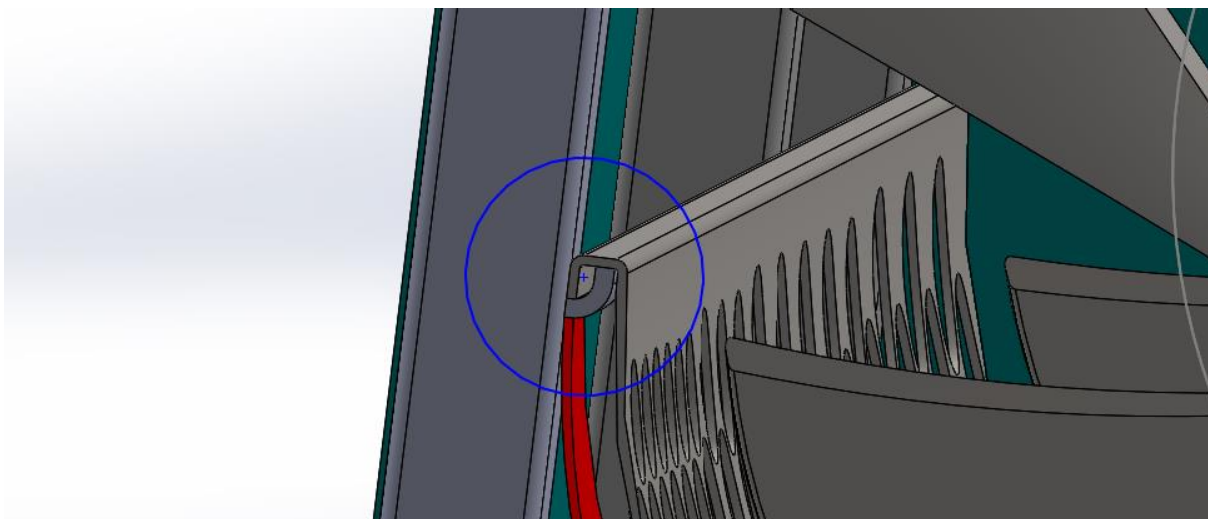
Detail vyspárování prostoru kolem podávacího šneku
